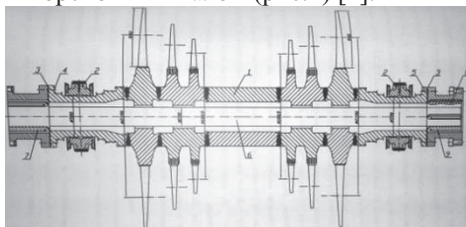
Сварной ротор и соосный вал ЦНД турбины Т-250/300-240
